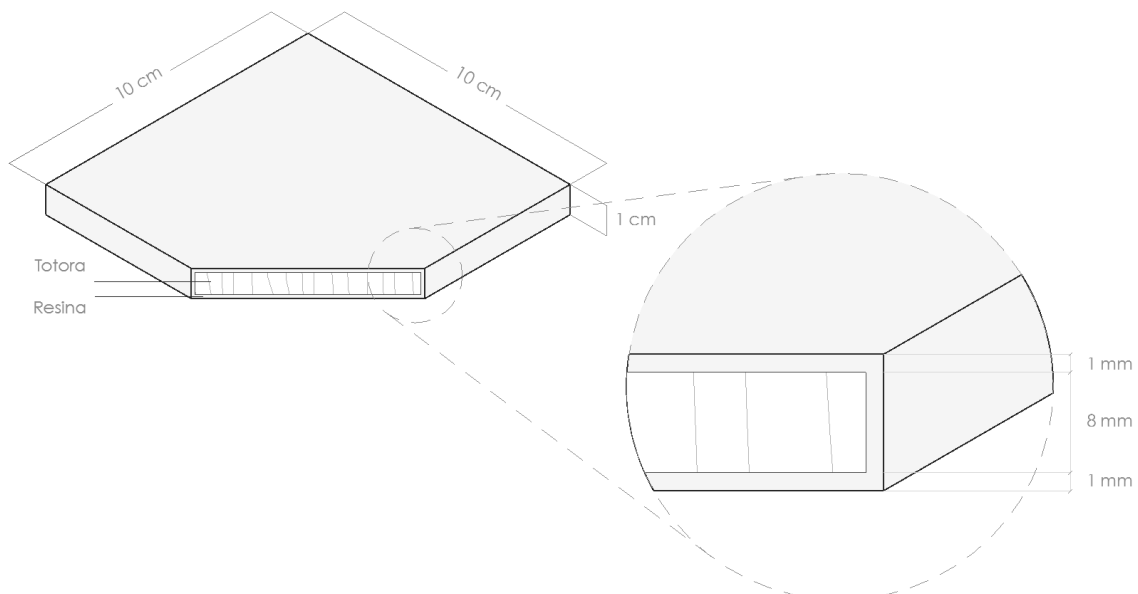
MUESTRA SECCIONADA, CON DIMENSIONES Y SU COMPOSICIÓN. FUENTE: PROPIA
